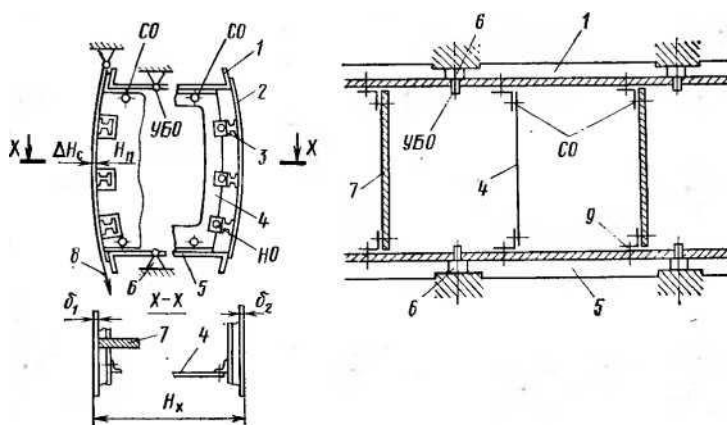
Схема базирования по внутренней поверхности обшивки
